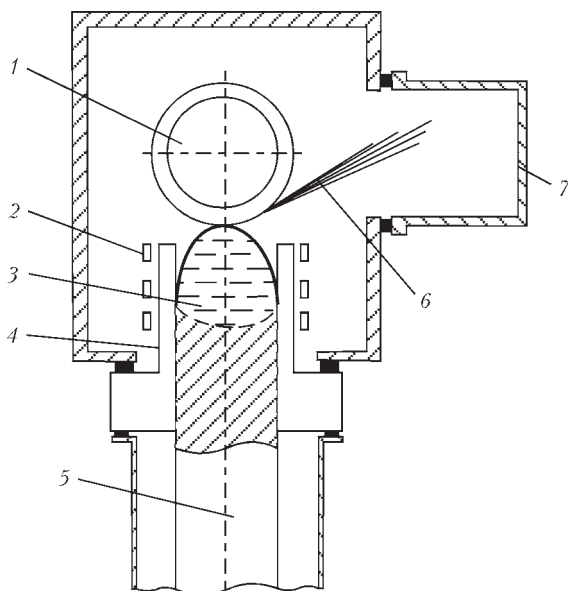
Принципиальная схема процесса экстракции из расплава: 1 — диск-кристаллизатор; 2 — индуктор; 3 — металлическая ванна; 4 — секционный кристаллизатор; 5 — расходимая заготовка; 6 — быстрозакаленные чешуйки, 7 — камера для сбора быстрозакаленных чешуек
